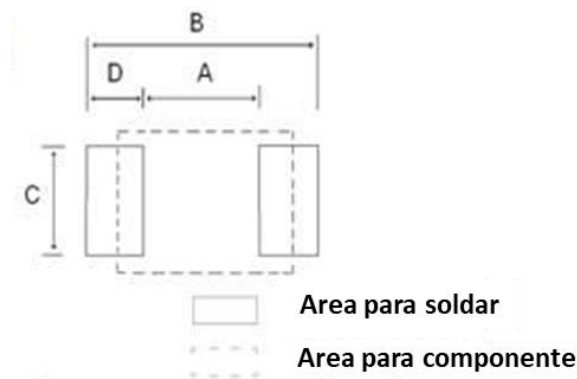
Áreas de soldadura. La figura muestra la definición de las áreas del componente y el área de soldadura de este en un circuito electrónico común.
